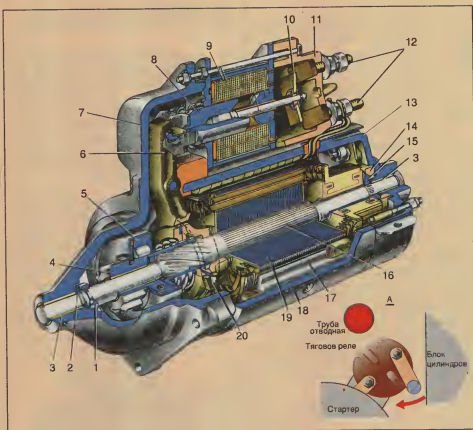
Конструкция стартера СТ-221: 1 – ограничительное кольцо; 2 – регулировочные шайбы; 3 – втулки; 4 – шестерня привода; 5 – обгонная муфта; 6 – двуплечий рычаг; 7 – крышка со стороны привода; 8 – якорь реле; 9 – обмотка реле; 10 – контактная пластина; 11 – крышка реле; 12 – контактные болты; 13 – задняя крышка; 14 – тормозящее кольцо; 15 – коническое кольцо вала; 16 – вал якоря; 17 – полюс; 18 – корпус; 19 – якорь стартера; 20 – поводящее кольцо.
